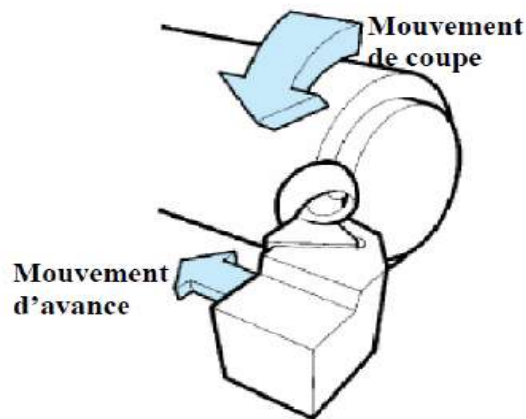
Mouvements de coupe et d'avance en tournage [2].
